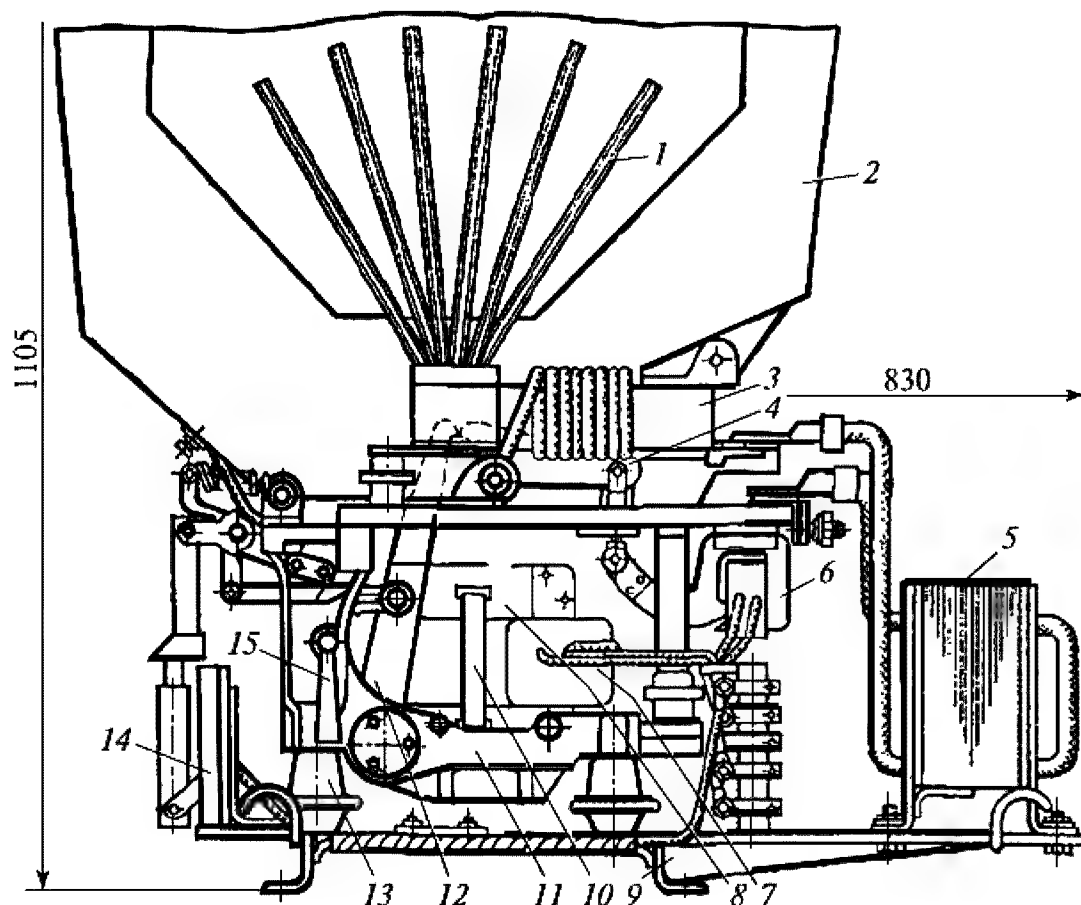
Малогабаритный быстродействующий выключатель БВЭ-ЦНИИ
